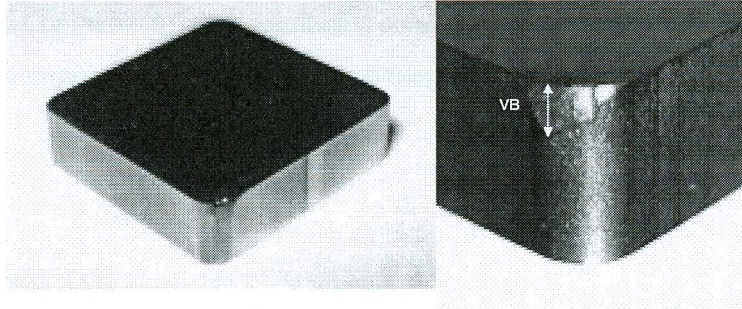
Desgaste de flanco (VB) na pastilha de aço rápido AISI T15.
